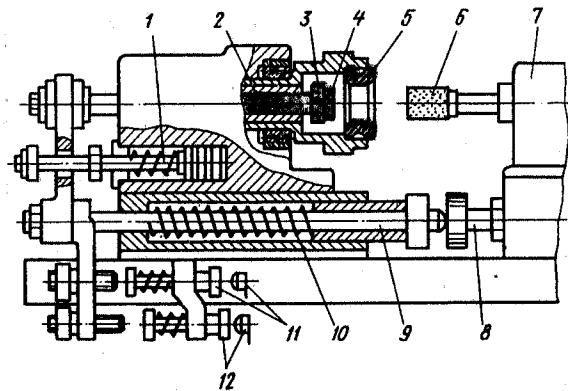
Устройство для контроля диаметра отверстия жесткими калибрами-пробками
